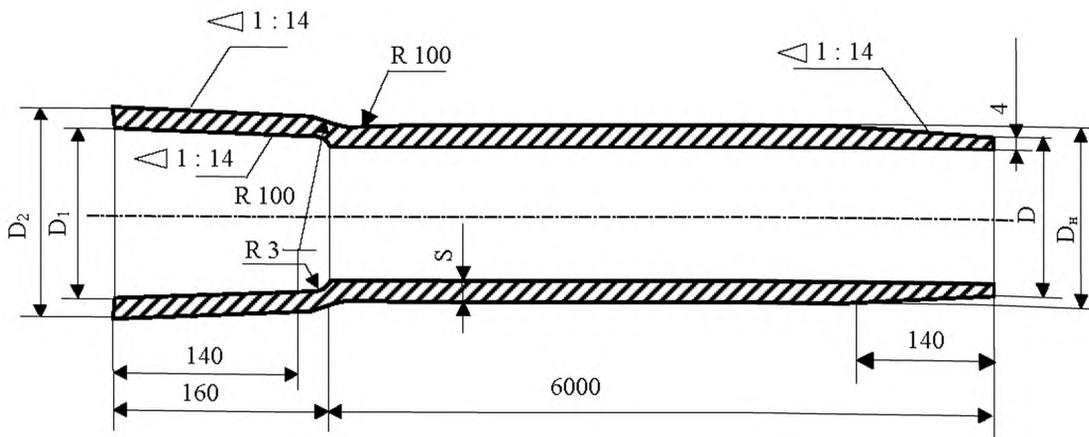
Труба под нахлестное сварное соединение
